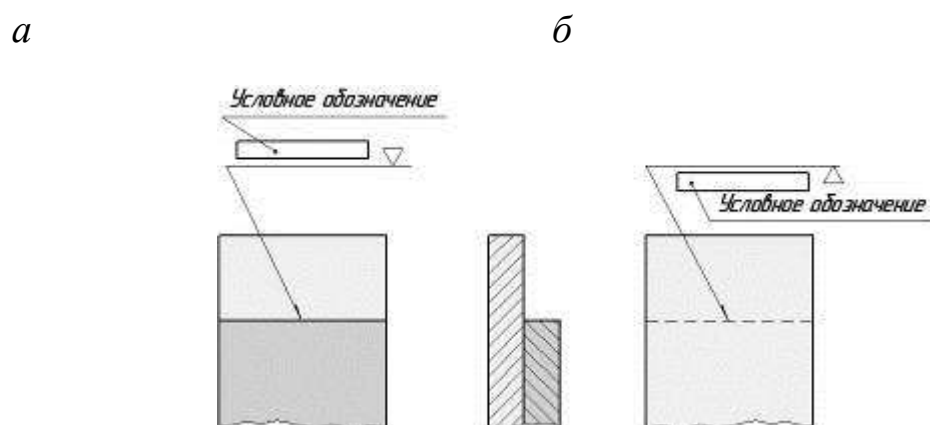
Изображение сварного шва: *а* – видимый шов; *б* – невидимый шов
